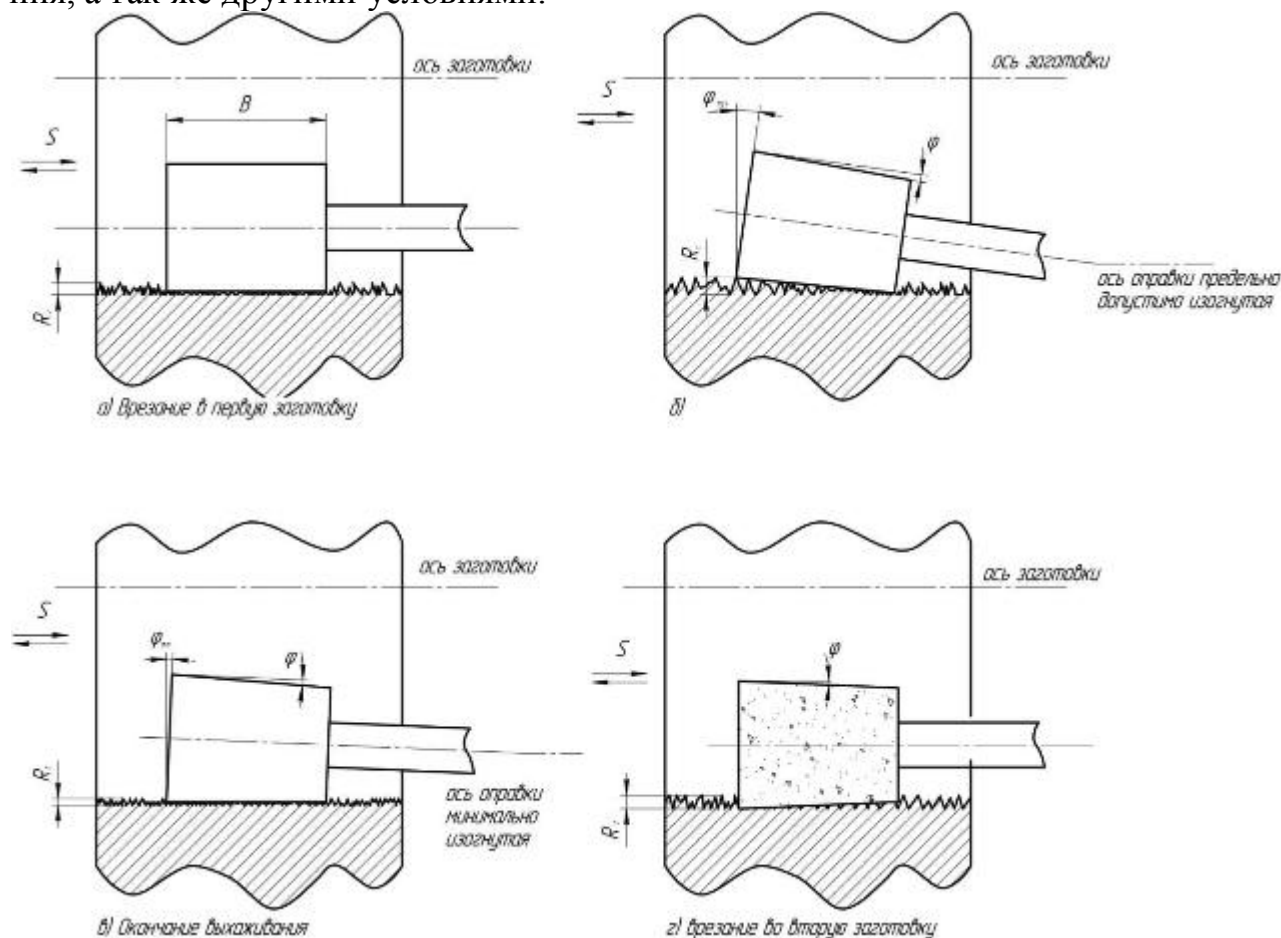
Положение приведенной цилиндрической поверхности легко прирабатываемого круга относительно заготовки.
